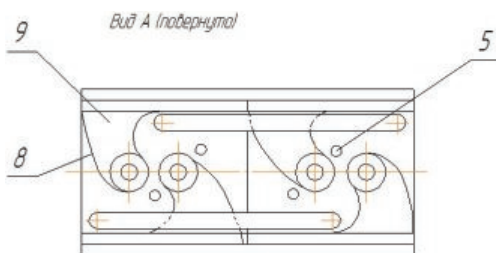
Устройство для тепловой обработки колбасных изделий (вид сверху)
